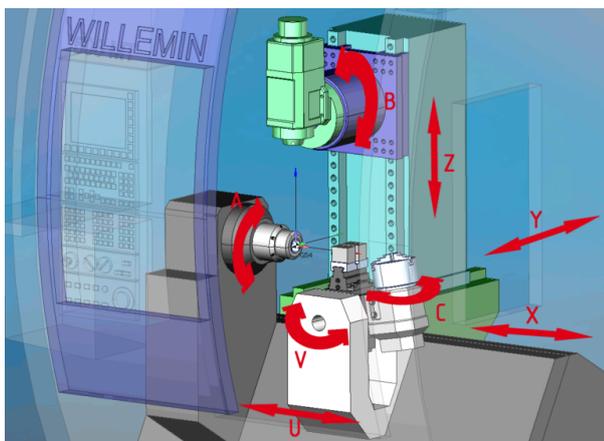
Схема станка Willemijn Macodel 508MT в SprutCAM
